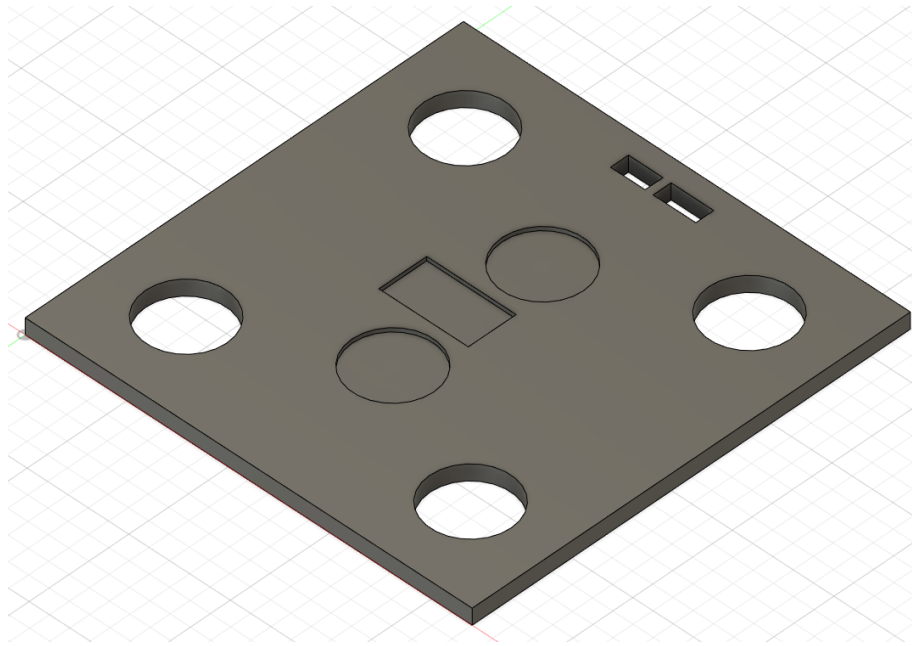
Нижня поверхня корпусу в тривимірному вигляді
